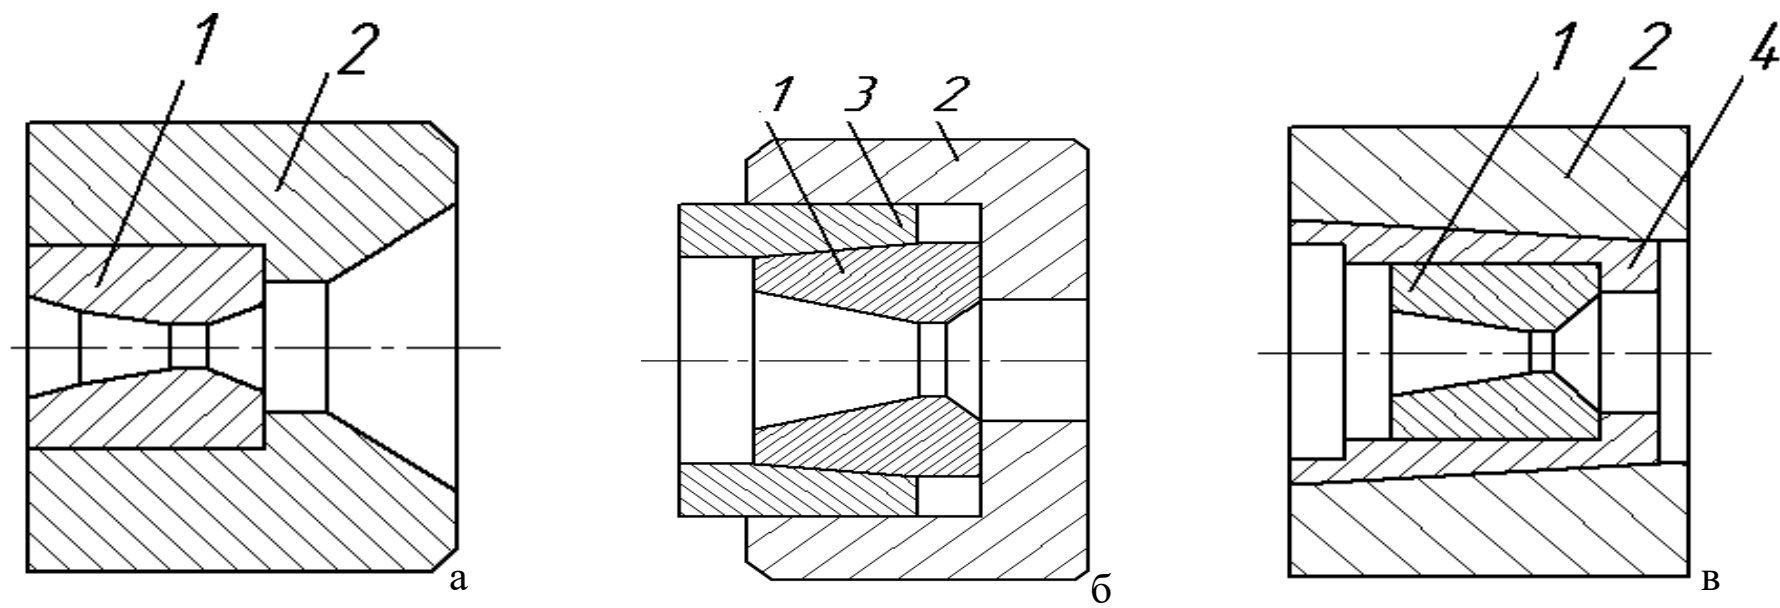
Одинарні волокни: 1 - тврдосплавний вкладиш (волокна); 2 - сталевий корпус; 3 - конусна суцільна втулка; 4 - затискна (цангова з розрізом) втулка.
